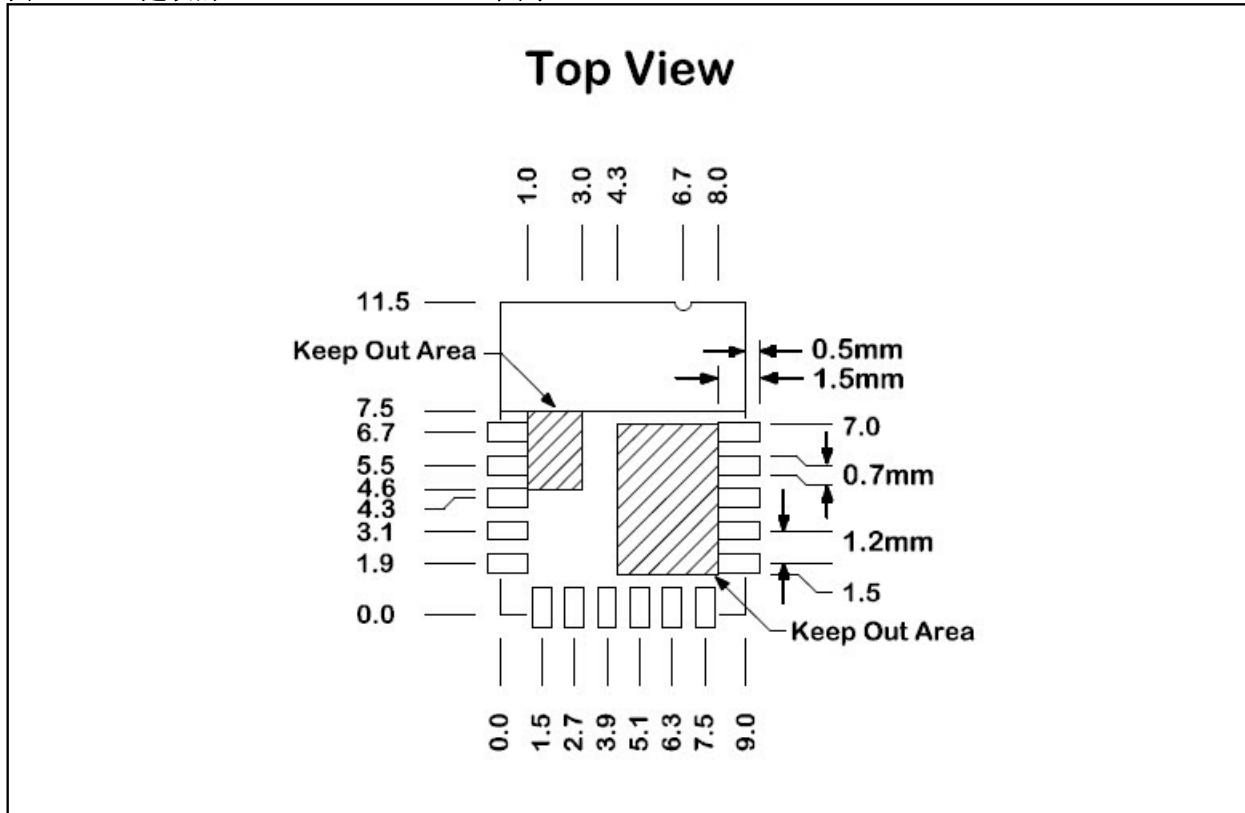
建议的 BM71BLES1FC2 PCB 尺寸
